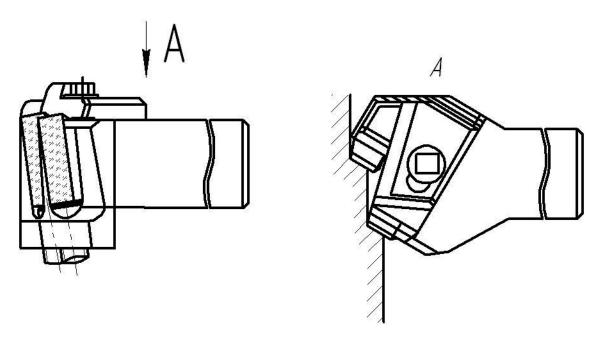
Резец с вертикальным расположением твёрдосплавной пластины
